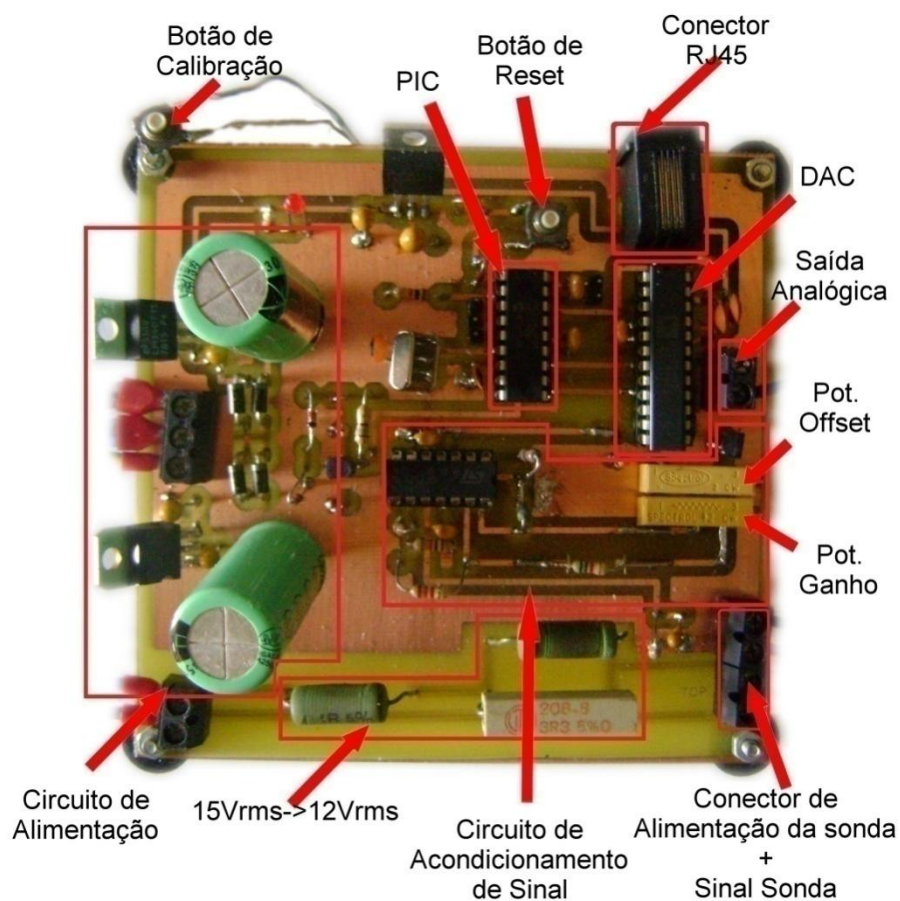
PLACA PCB COM O BOTÃO DE CALIBRAÇÃO
